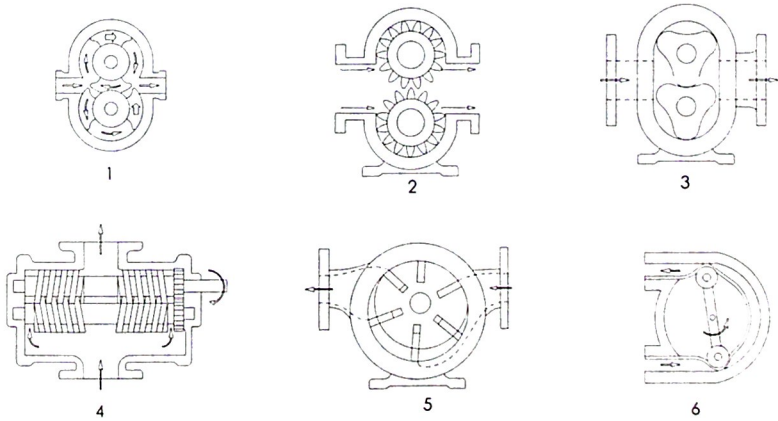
Bombas rotativas. 1) Pistón circunferencial; 2) Engranajes; 3) Lóbulos; 4) Tornillo; 5) Paleta deslizante; 6) Peristáltica.
